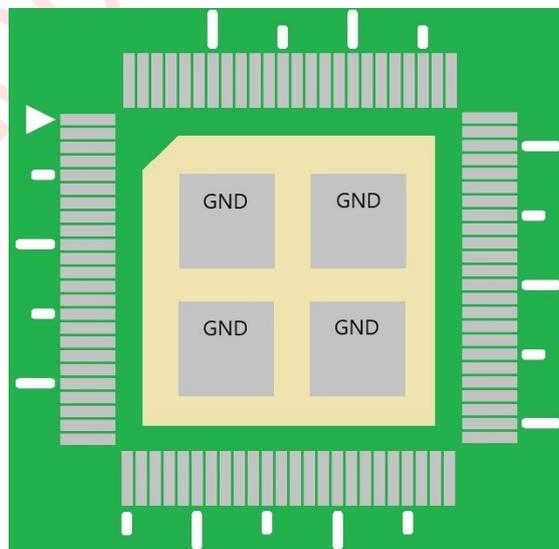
LT7589A 底部焊盘 PCB 的设计建议-2
